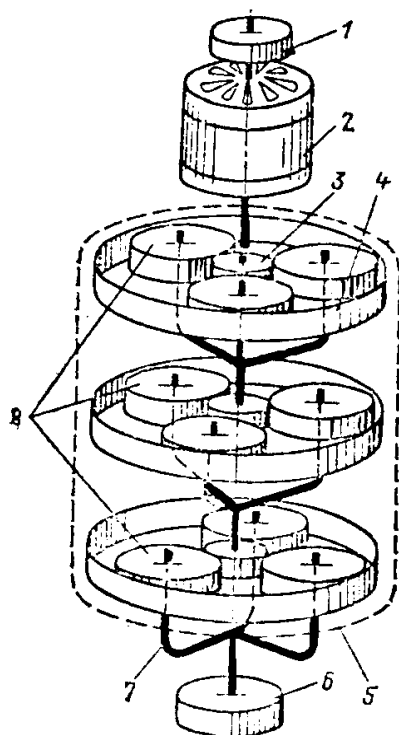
Схема механизма поворота башенного крана с планетарным редуктором
